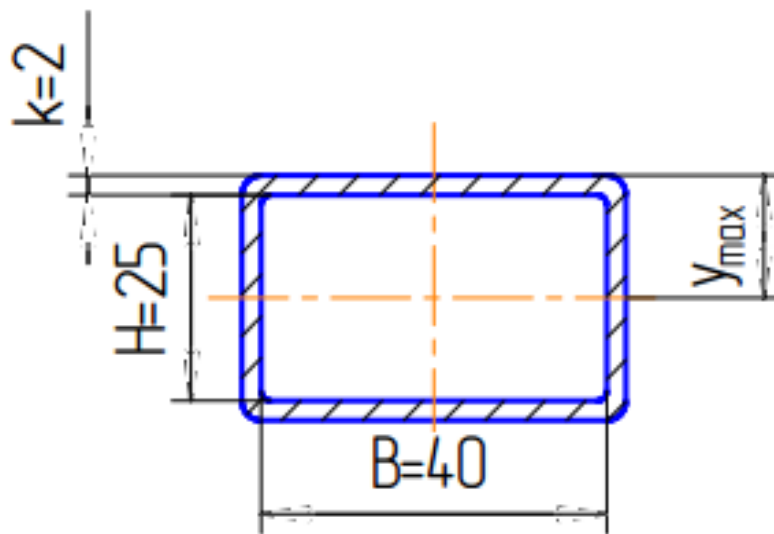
Розрахунковий переріз зварного з'єднання
